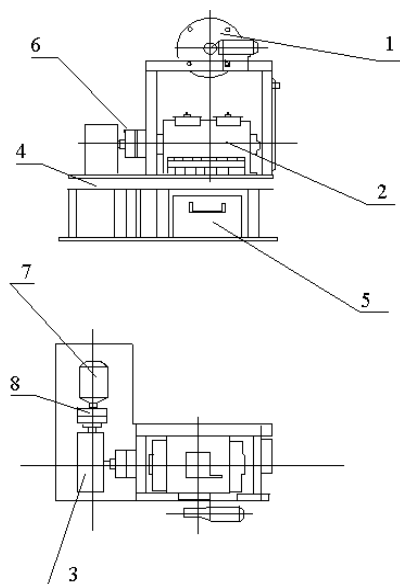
Схема лабораторной установки: 1 - верхний смеситель (связующего); 2 - нижний смеситель; 3-редуктор; 4-рама; 5 - ящик; 6 - укрытие муфт; 7 - двигатель; 8 – муфта
